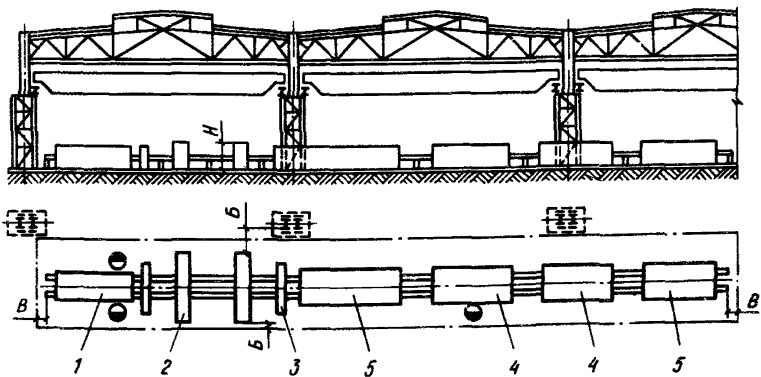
Размещение поточной линии для сборки и сварки подкрановых балок
